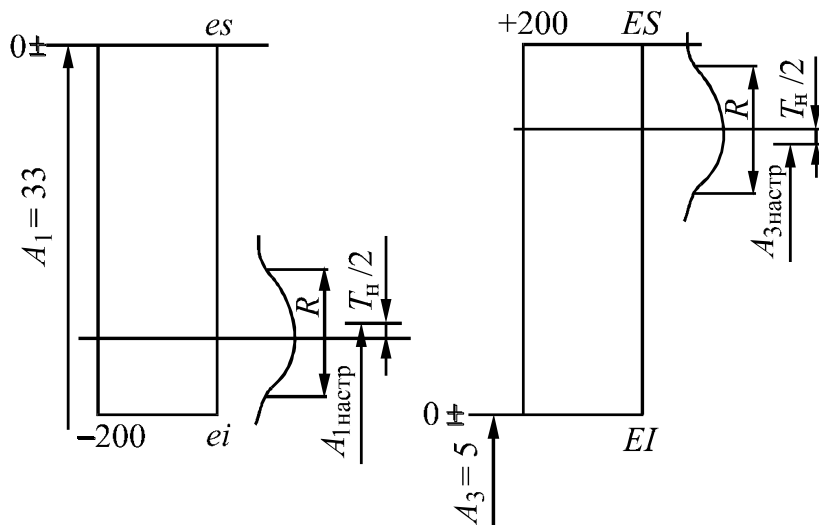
Схема расположения полей допусков на изготовление детали при фрезеровании шпоночного паза
